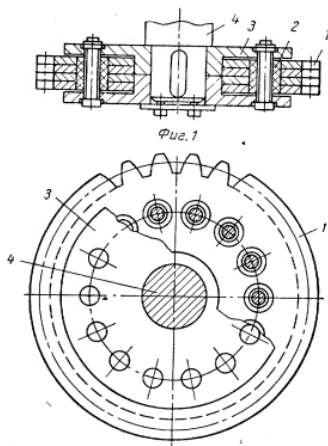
Колесо, що складається з пакету зубчастих дисків
